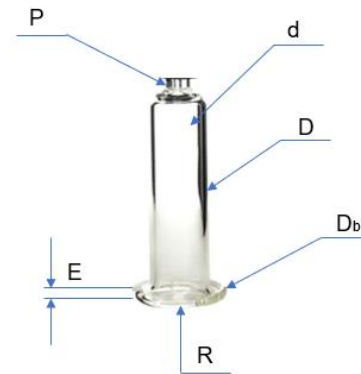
Partes a inspeccionar en la Jeringa de insulina
